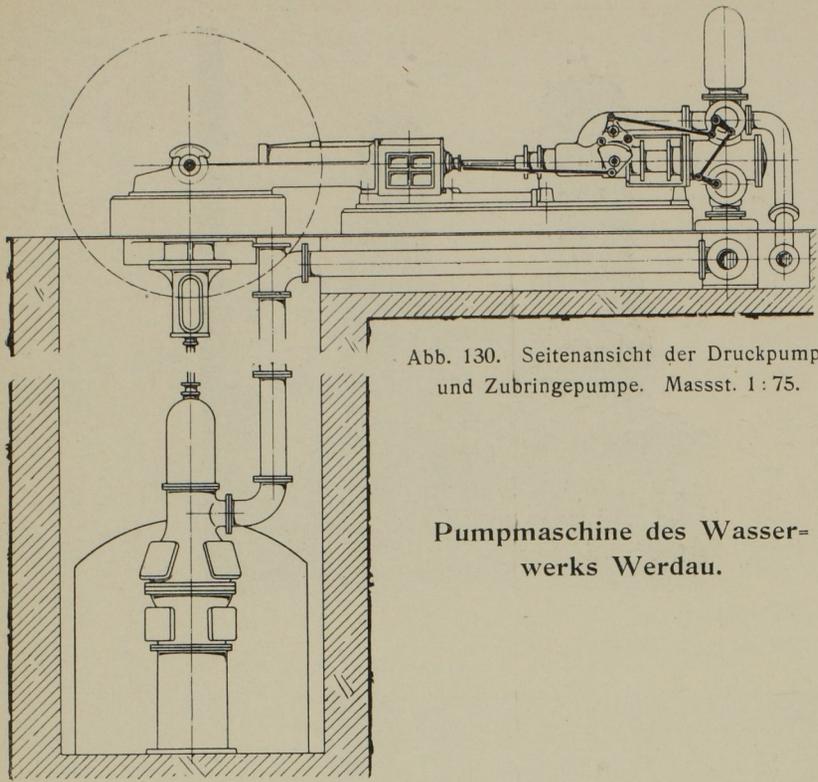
Seitenansicht der Druckpumpe und Zubringepumpe. Masst. 1:75.
